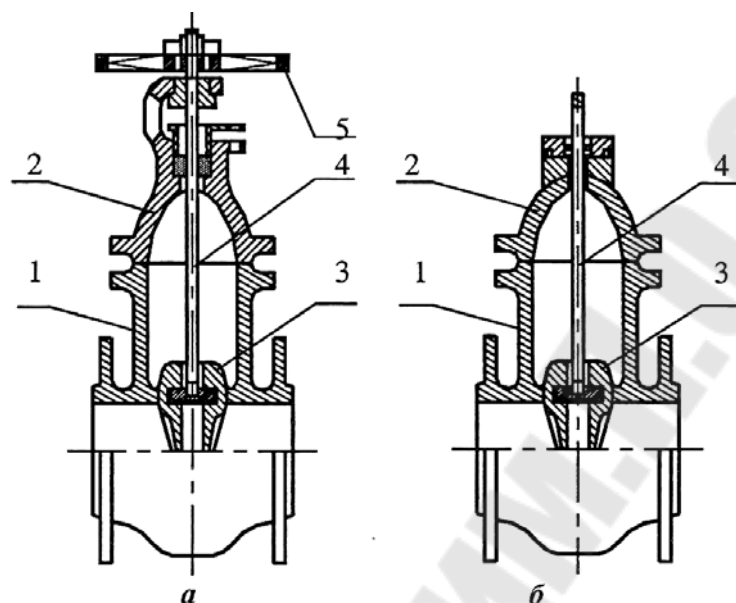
Затворки: а - клиновая с выдвижным шпindelем, б - клиновая с невыдвижным шпindelем; 1 - корпус, 2 - крышка, 3 - клин (затвор), 4 - шпindel, 5 - маховик
